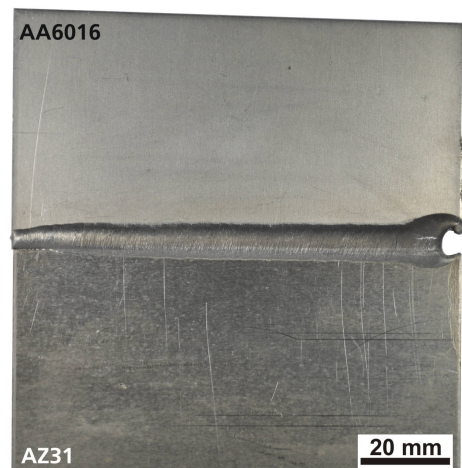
Fotografische Aufnahme der geschweißten coldArc®-Verbindung, AA6016 / AZ31 / AlSi12, Schweißnahtunterseite
